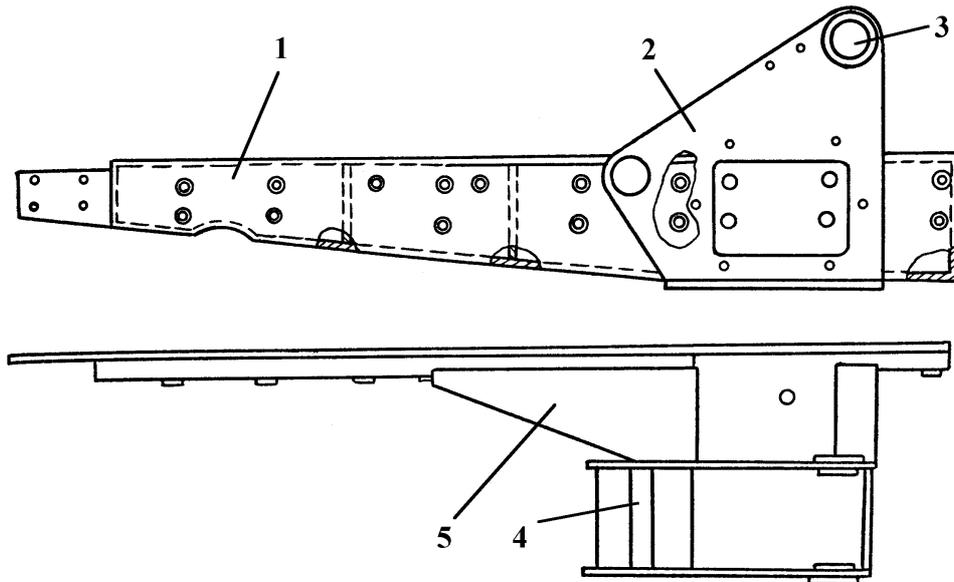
Рама погрузочного оборудования машин МТП-441, 441-01: 1 – пластина; 2 – серьга; 3 – проушина; 4 – поперечина; 5 – косынка
